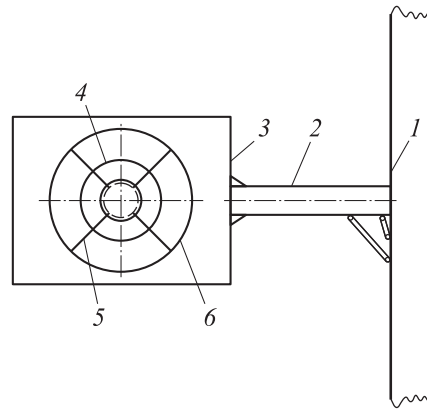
Схема оборудования, реализующего симметричный способ подачи: 1 — базовая машина; 2 — выносная штанга с распределительным оборудованием; 3 — бункер; 4 — лоток с кольцевой формой поперечного сечения; 5 — лопатки диска; 6 — распределительный диск
